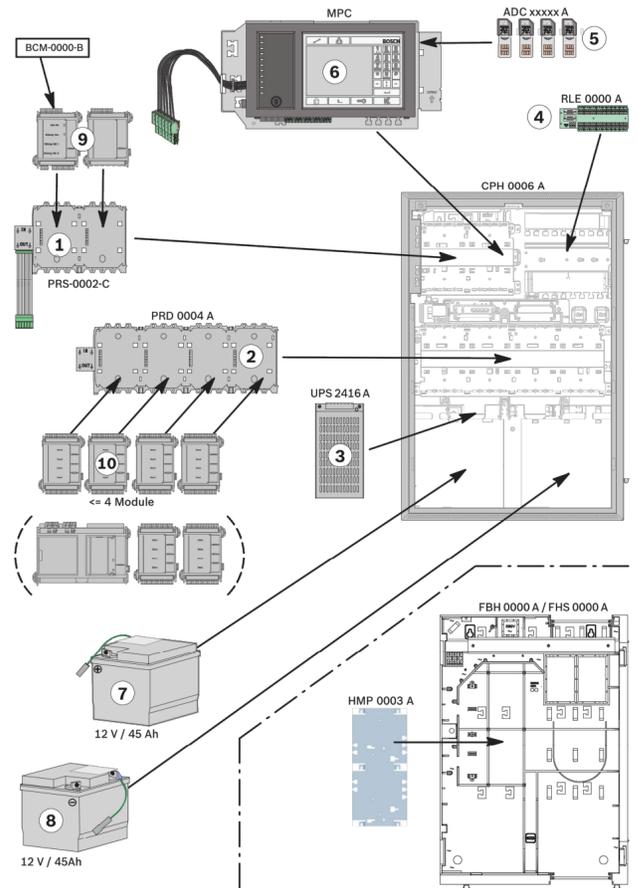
Пример компоновки корпуса для установки в раму СРН 0006 А для 6 модулей
